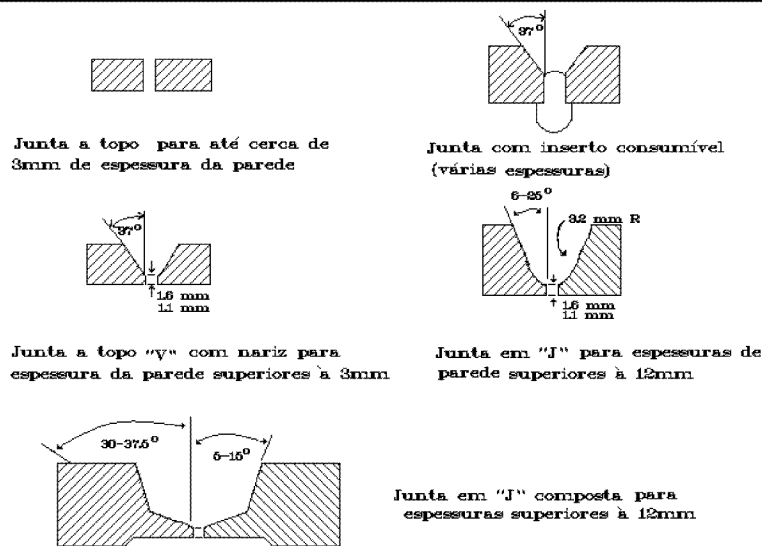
Juntas em Tubos para Soldagem com TIG Orbital.
